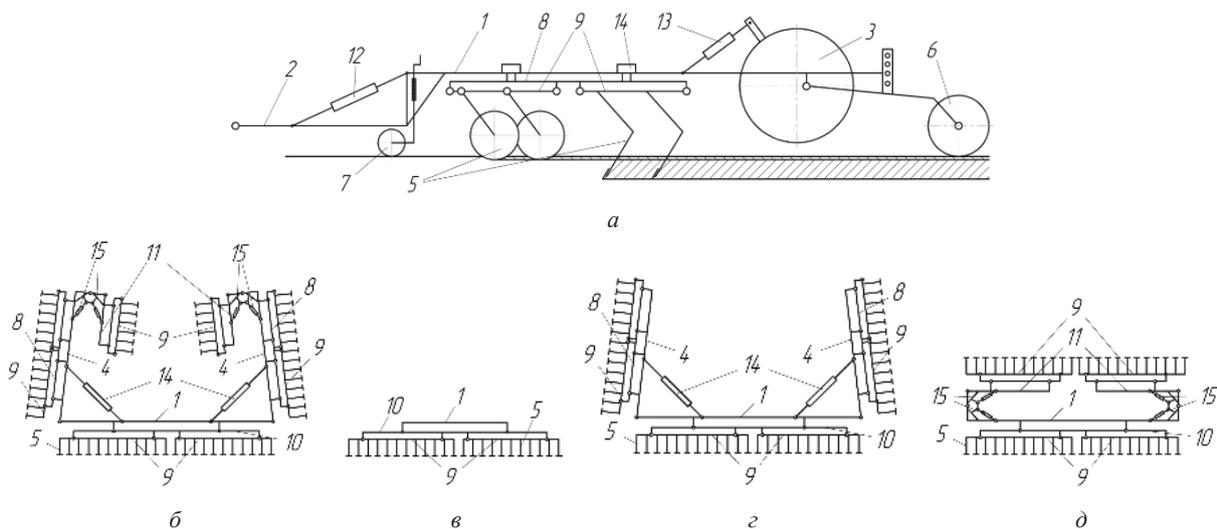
Схема почвообрабатывающего агрегата с изменяемой шириной захвата: *а* – агрегат, вид сбоку; *б* – агрегат с присоединенными боковыми и периферийными боковыми секциями, вид сзади; *в* – агрегат отсоединенными боковыми секциями, вид сзади; *г* – агрегат с присоединенными боковыми секциями, вид сзади; *д* – агрегат с периферийными секциями, вид сзади; 1 – рама; 2 – сница; 3 – транспортная тележка; 4 – боковая секция; 5 – почвообрабатывающие органы; 6 – каток; 7 – опорные колеса; 8 – заменяемый модуль; 9 – сменный подмодуль; 10 – средняя секция; 11 – периферийная секция; 12, 13, 14, 15 – гидроцилиндр
